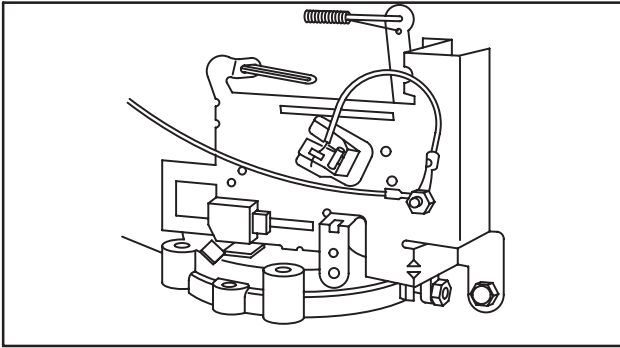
194700, 195700, 196700, 254700, 257700, 258700, 259700, 28A700, 28B700, 28C700, 28D700, 28E700, 28M700, 282700, 283700, 285700, 286700, 288700, 289700 avec commande à crémaillère horizontale pour carburateurs LMT Briggs & Stratton/Walbro
